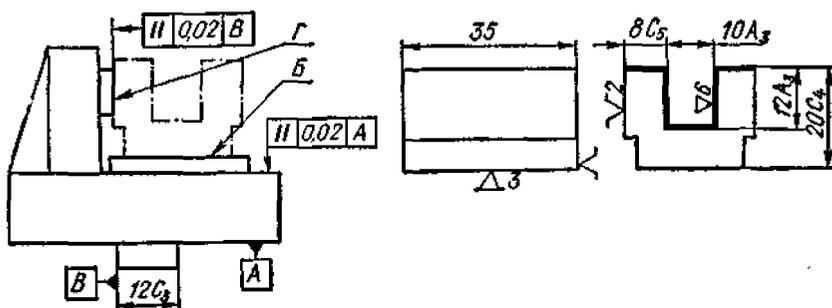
Схема для расчета допуска на изготовление фрезерного приспособления
